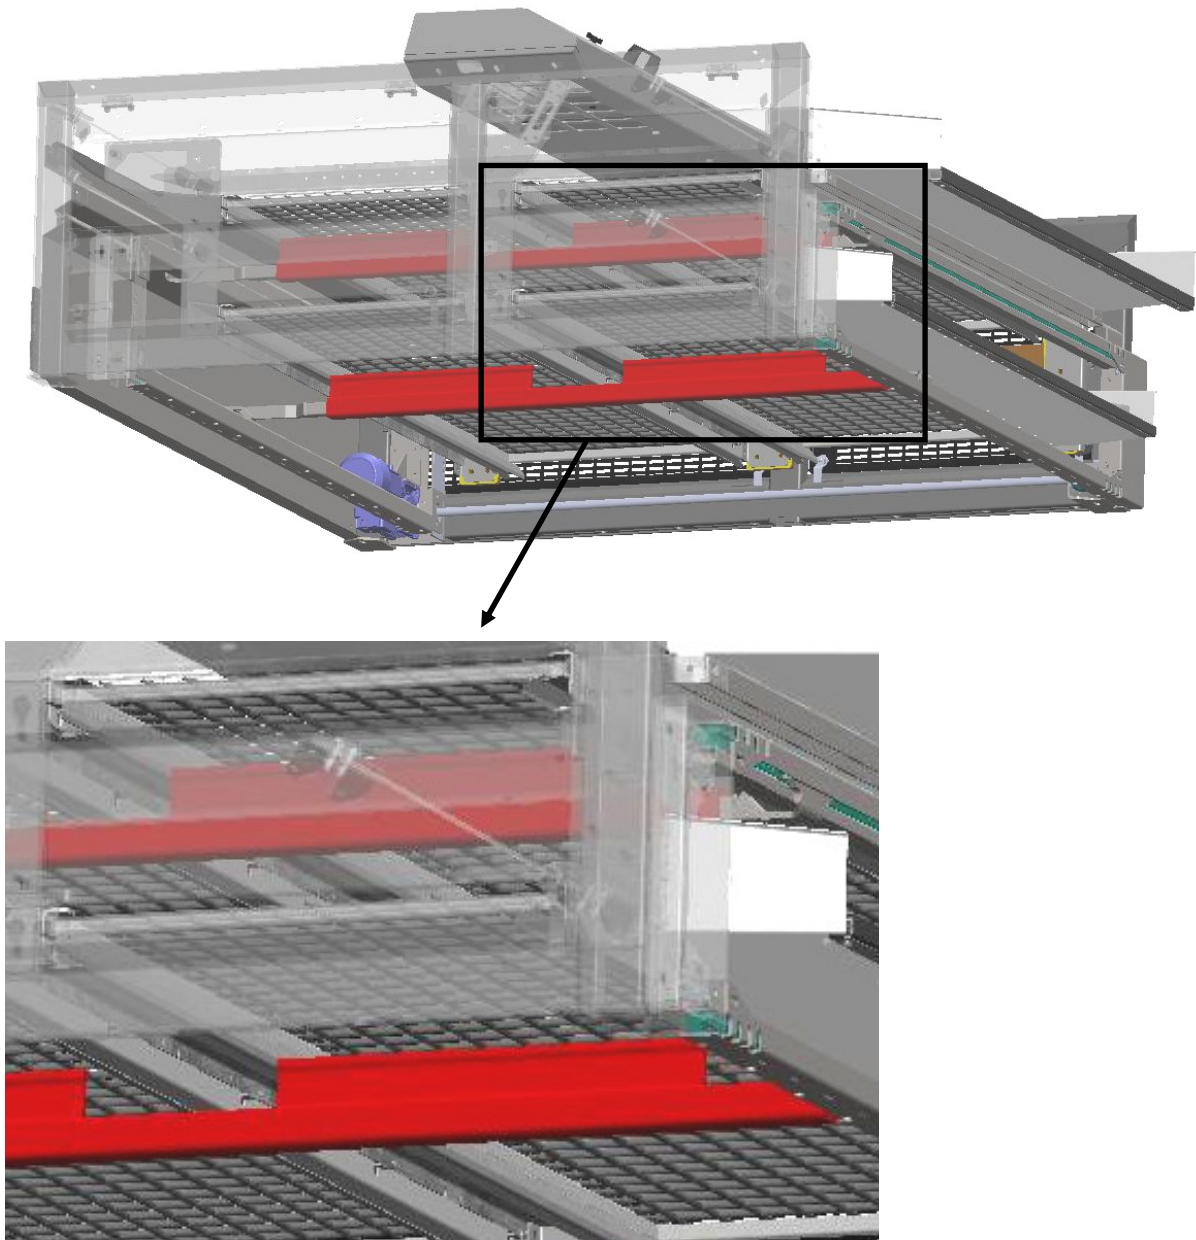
zeigt die Platzierung der „Spritzenschläuche“, die die Siebe in ihrer Position im Siebkasten halten.
